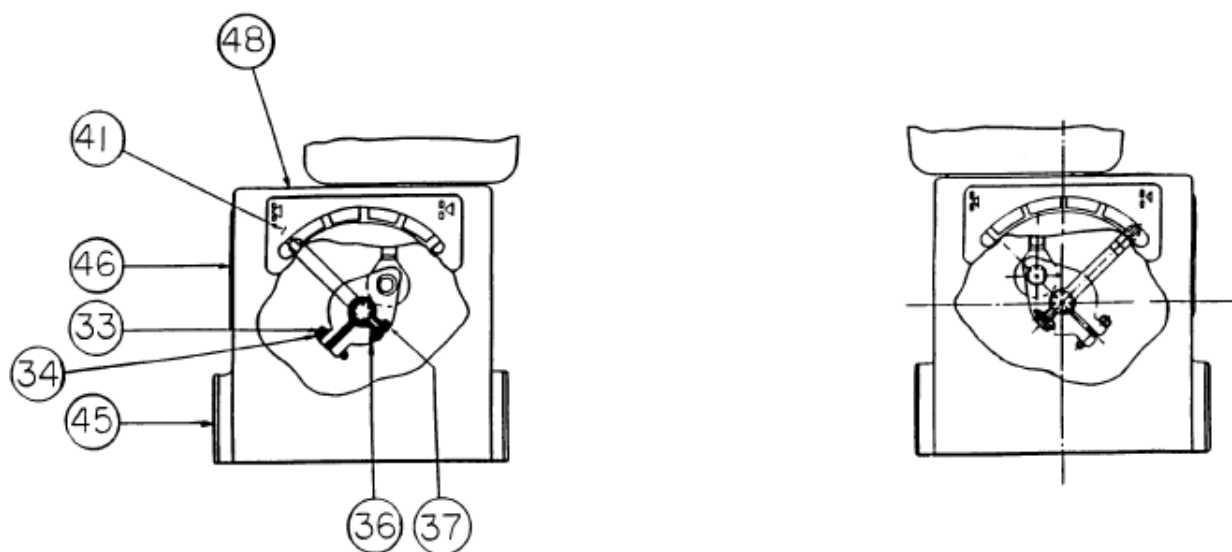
Деталировочный чертеж индикатора положения. Приводы размера В и С
